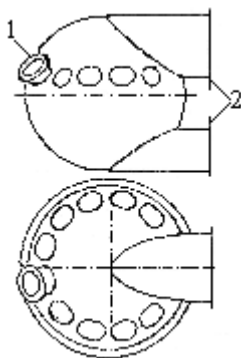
Шаровой коллектор: 1 – патрубок для присоединения ответвления (входной); 2 – патрубки для присоединения транспортного трубопровода (снизу) и трубопровода отбора воздуха (сверху)
